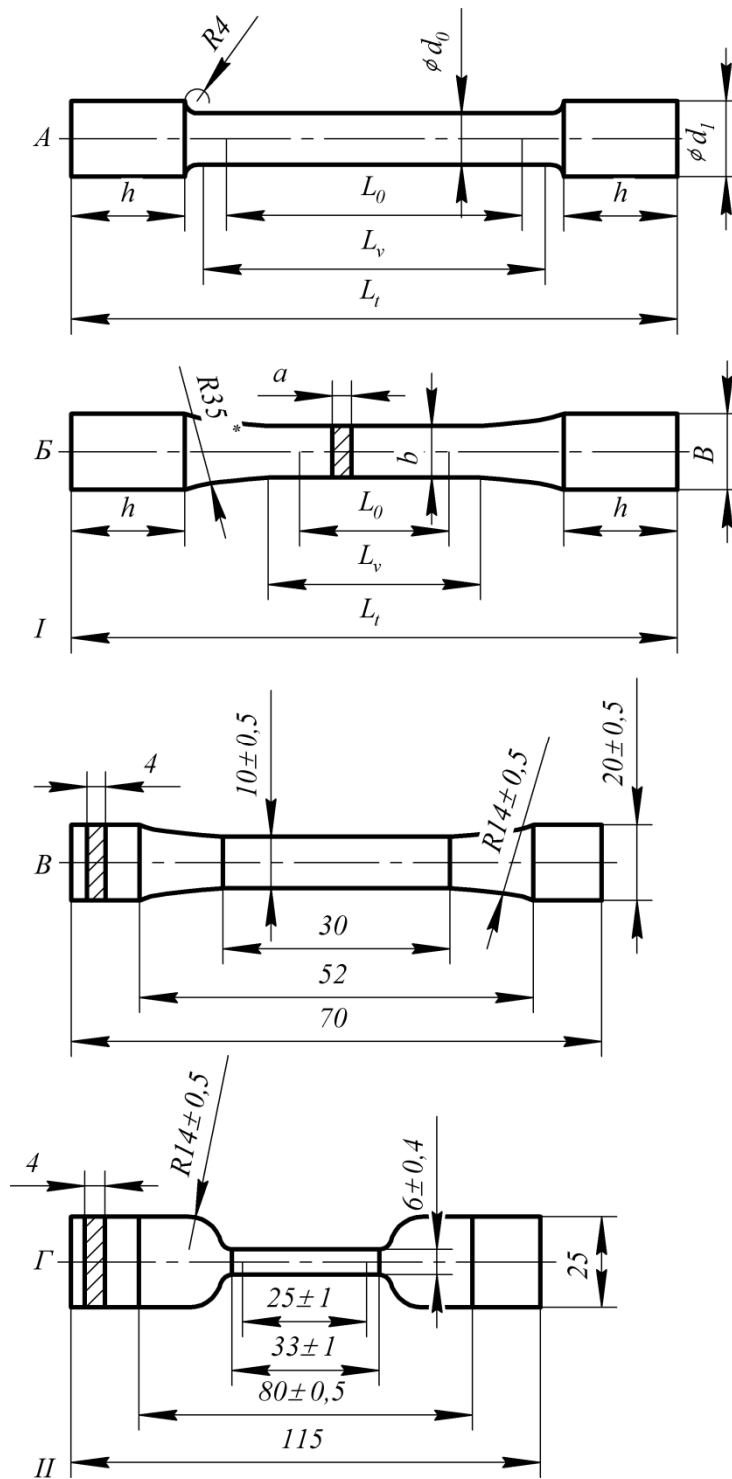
Образцы для испытаний на растяжение: I – металлические материалы: А – цилиндрический образец с гладкой цилиндрической головкой; d_0 – диаметр образца; L_0 – расчетная длина образца; $d_1 \approx 1,2d_0$ – диаметр головки; $L_V = L_0 + d_0$ – длина образца, испытываемого на растяжение; L_t – общая длина; h – высота головки; Б – плоский образец с гладкой головкой: a – толщина образца; b – ширина образца; $B = 1,2b - 3$ мм – ширина головки; $h \approx 2b - 10$ мм – высота головки; II – полимерные материалы: Б; В и Г – образцы материала с небольшой и большой деформацией при разрушении соответственно
